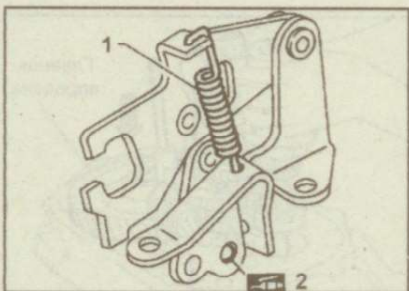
Установка пружины (1) и шарика (2) на рычаг передачи заднего хода
